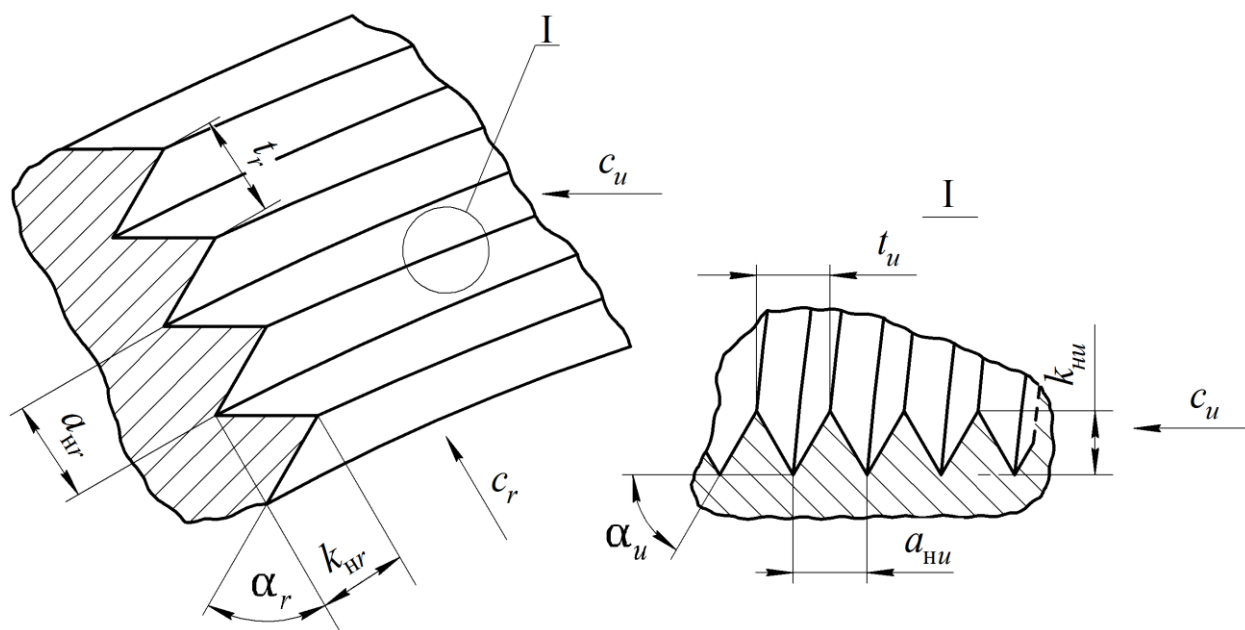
Натурная шероховатость поверхностей дисков и корпуса;
